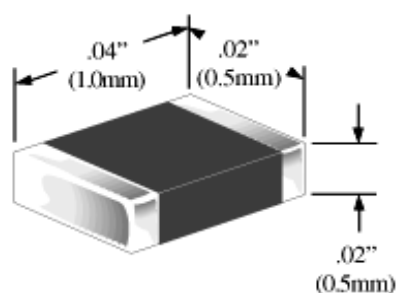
Габаритні розміри резистора типу 0402
